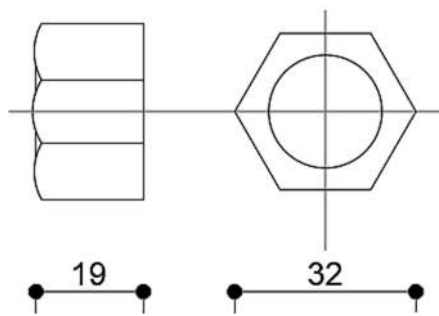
Detail Sambungan Spesimen Tipe PS-3
